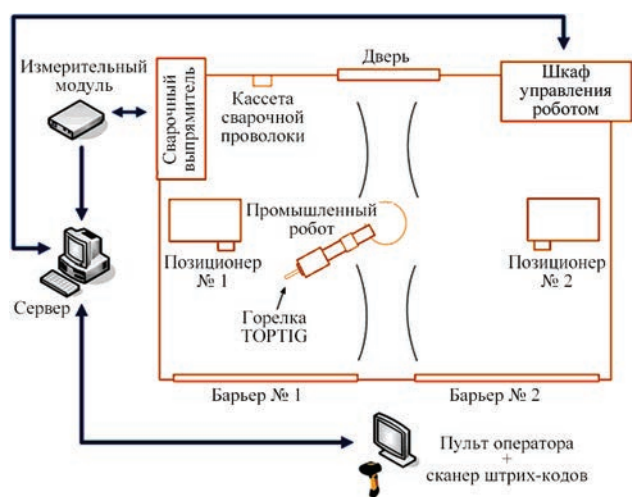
Планировка поста роботизированной сварки ТОРТІG с системой контроля параметров сварки
